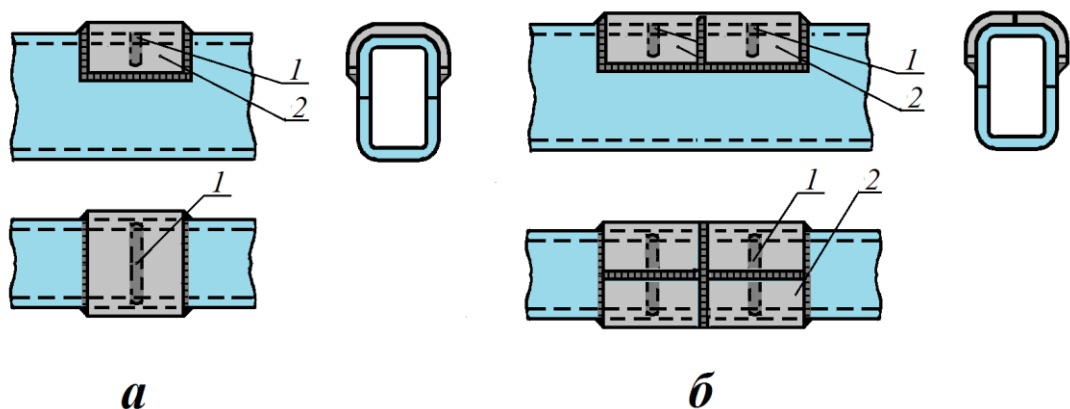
Схема підготовки до зварювання тріщин в елементах типу зварних балок коробчатого перерізу
